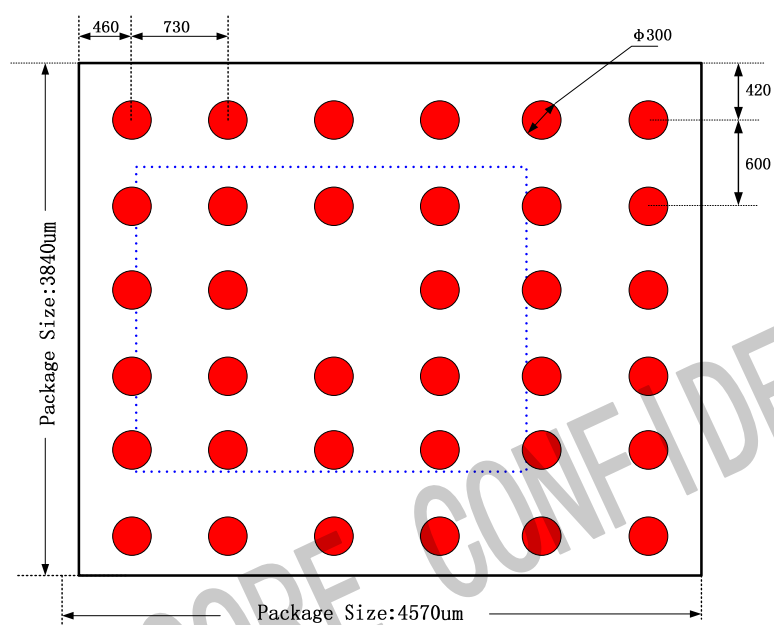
PCB 焊盘设计说明示意图(Top view)
